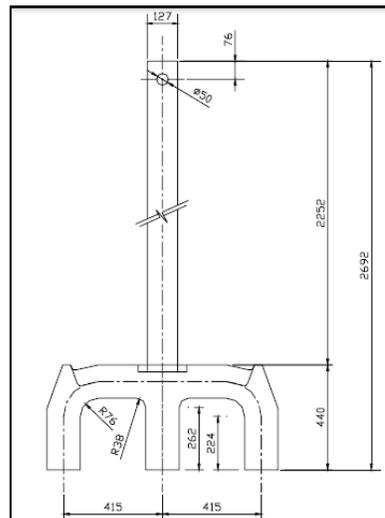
El plano muestra dimensiones de la varilla utilizada en CVG Venalum Medidas en mm.
